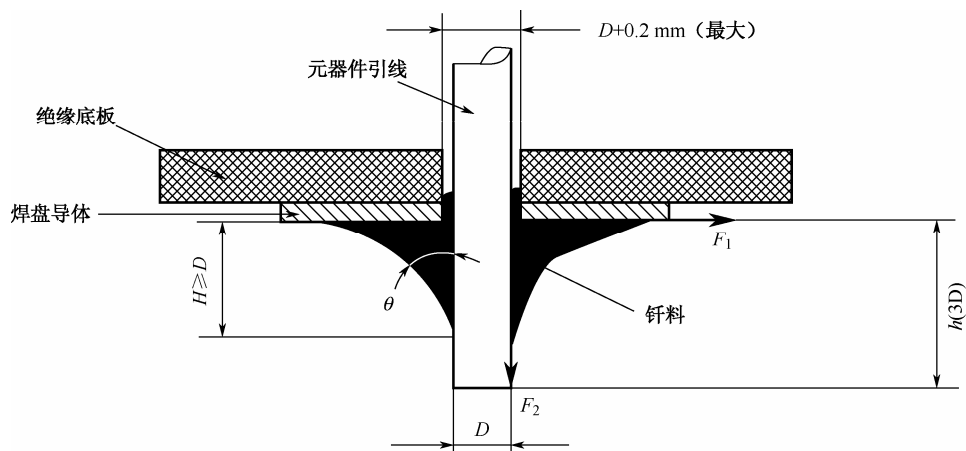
无金属化孔单面 PCB 理想圆角或润湿角及浸润高度的构成条件
